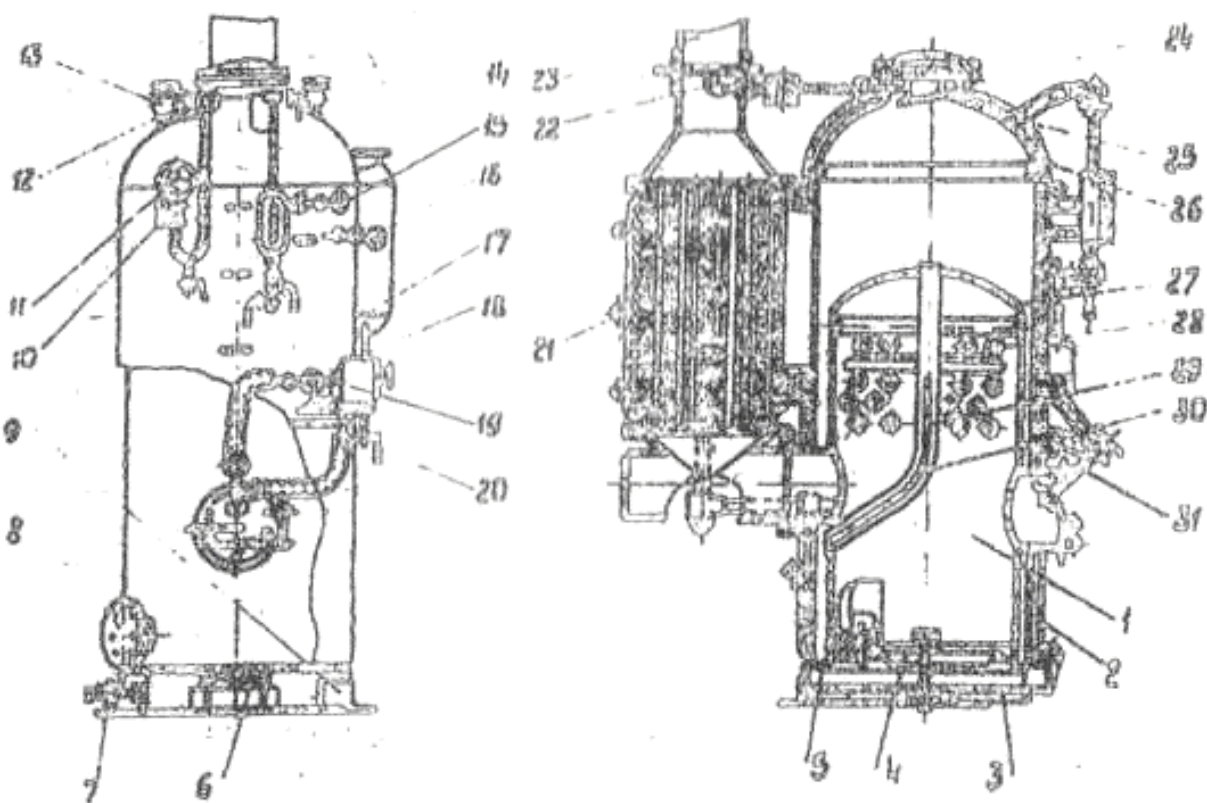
Схема парового котла РИ-5М: 1-жаревая труба, 2-корпус котла, 3-поддон, 4-колосниковая решетка, 5-упорное кольцо, 5-дверца зольника, 6-вентиль для отпуска воды из котла, 7-спускной патрубков, 8-опорное полукольцо, 9-трехходовой кран, 10-манометр, 11-главный запорный вентиль, 12-предохранительный клапан, 13-водоуказательное стекло, 14-верхний водопроводный кран, 15-нижний водопроводный кран, 16-бачок для жидкого топлива, 17-вентиль для пуска топлива в форсунку, 18-конденсационный бачок, 19- краник для спуска конденсата, 20-водо подогреватель, 21-сифон, 22-дымовая труба, 23-смотровой люк, 24-сепаратор, 25-копия котла, 26-днище топки, 27-поперечные кипящие трубы, 28-вертикальные кипящие трубы, 29-перегородка, 30-форсунка.
